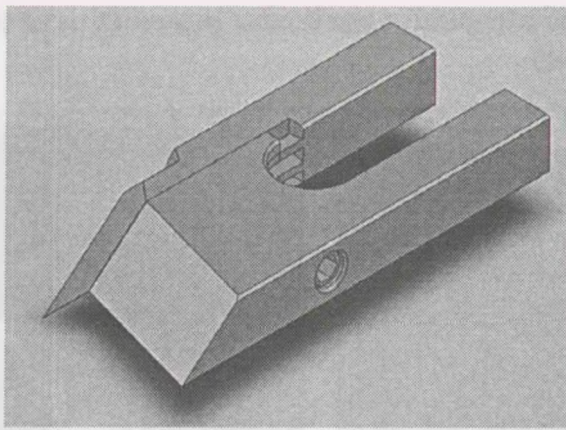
Сборный двухлезвийный нож фрезерно-брусующего станка
